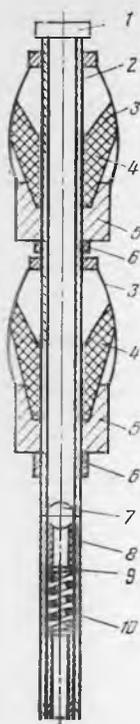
Сваб с регулируемым клапаном конструкции «Азин-маш»:
